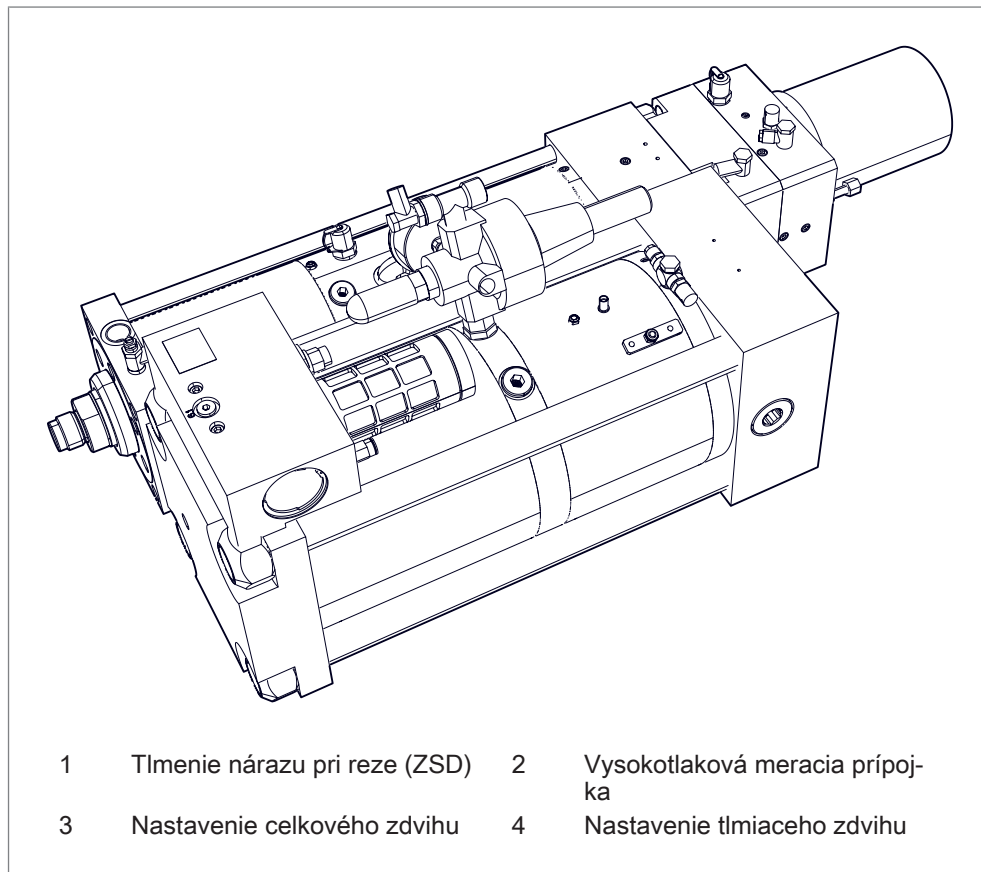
Prehľad výrobkov Kraftpaket s integrovanou funkciou tlmenia
